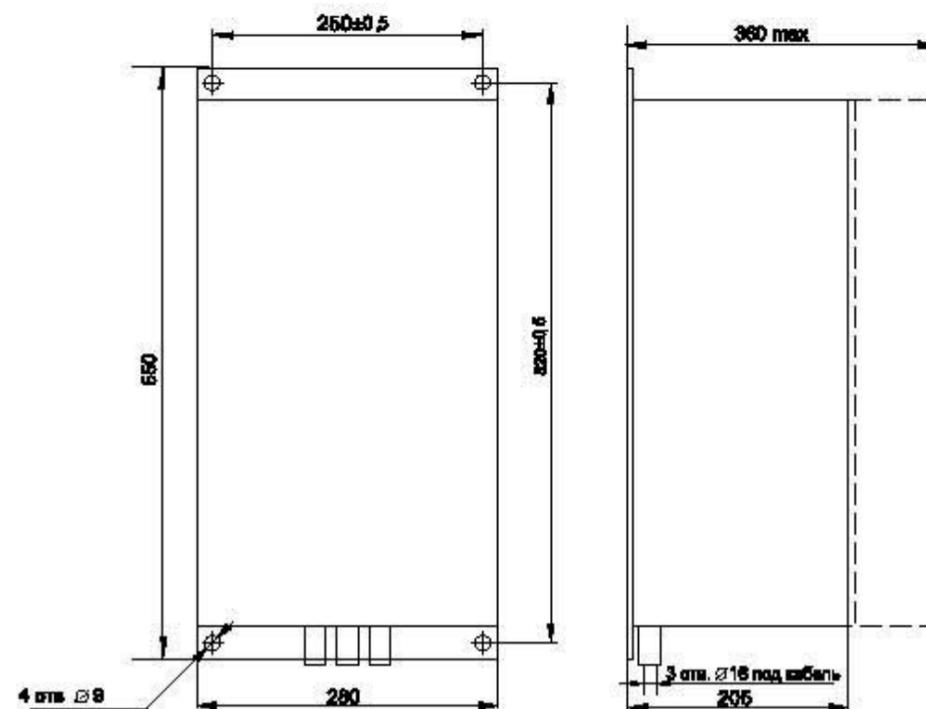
Габаритные и установочные размеры стабилизатора напряжения ИСН-М
